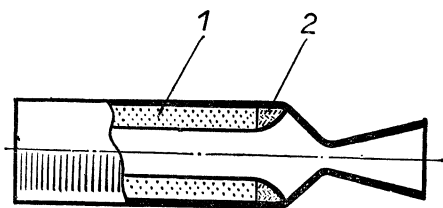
Схематическое изображение ракетного двигателя на твердом топливе:
